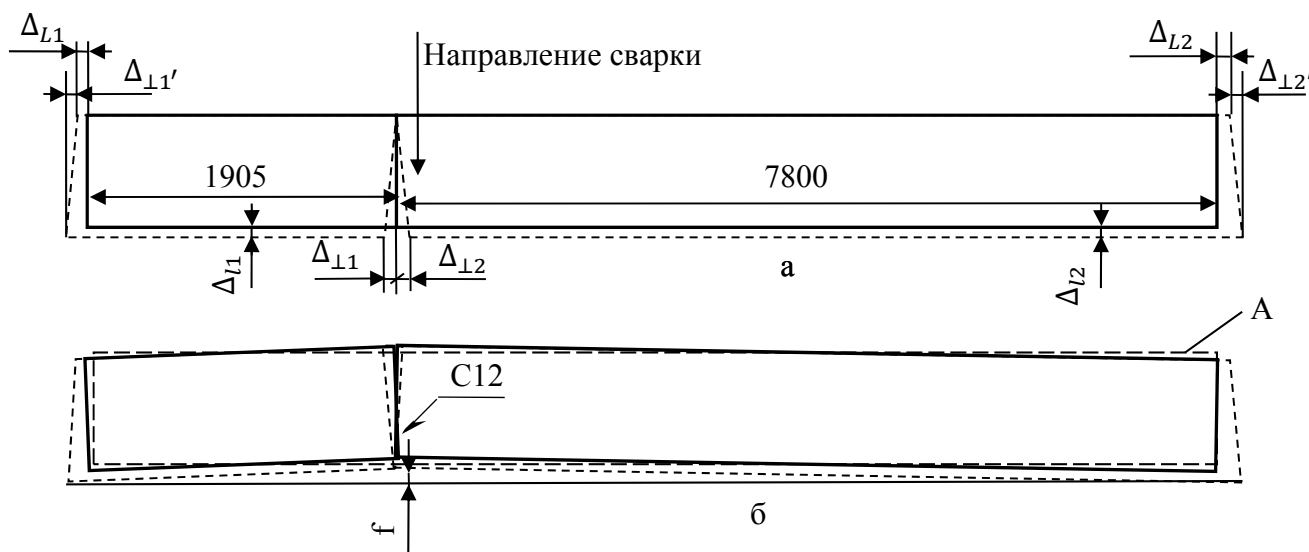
Допуски размерных цепей третьего порядка:
